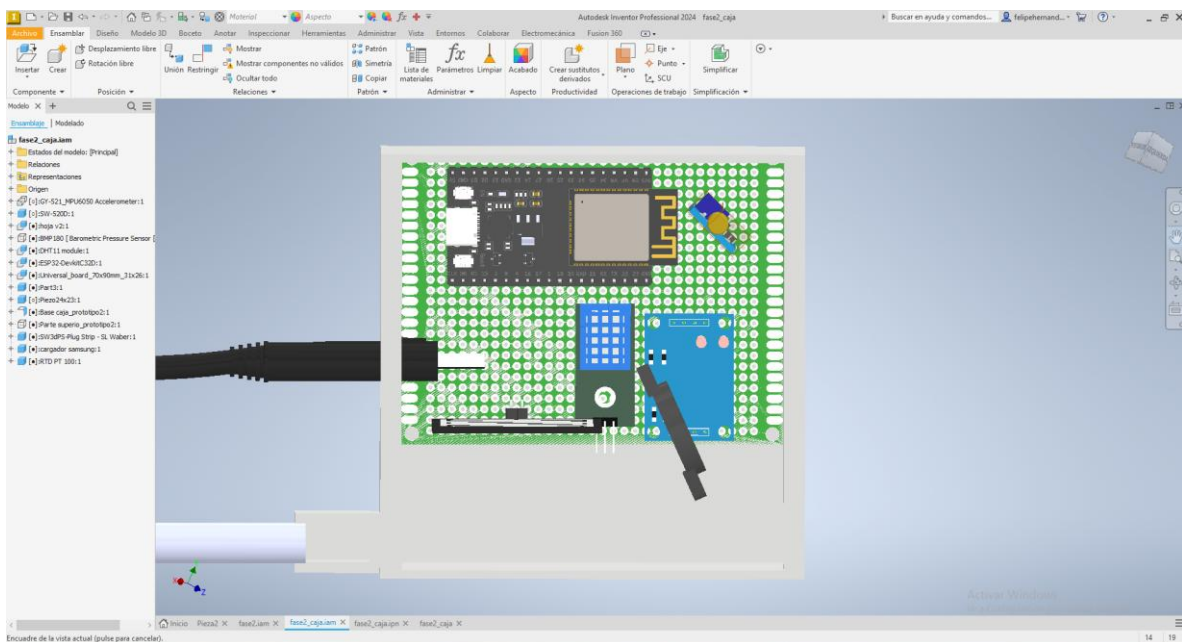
Diseño CAD del prototipo mecánico Vista superior
